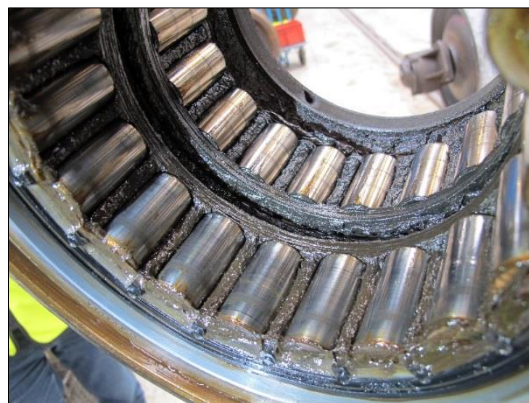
Innerring fra indre lager med skråstilt rulle. Foto: SHK
